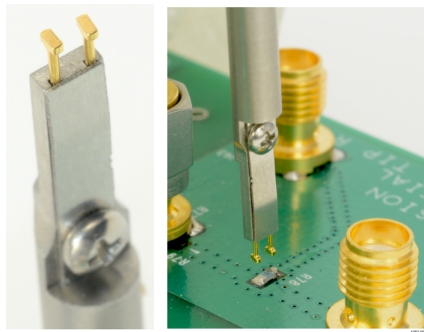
Uso del auxiliar de soldadura para instalar los terminales de prueba en la placa de circuitos
